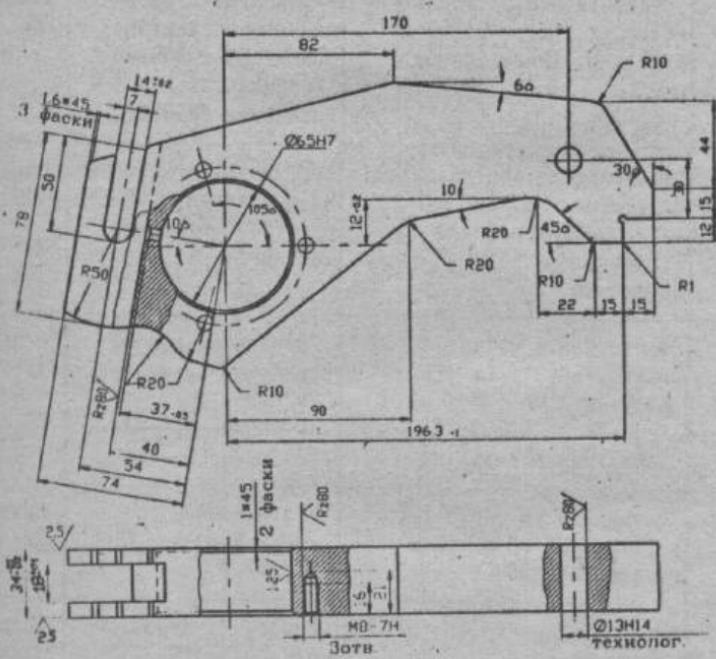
Вазіль (вид заготовки - лист, матеріал - сталь20Х, кількість деталей із заготовки - 1)
